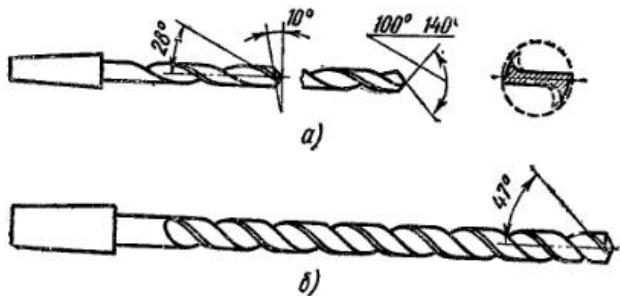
Сверло для сверления отверстий в магниевых сплавах
